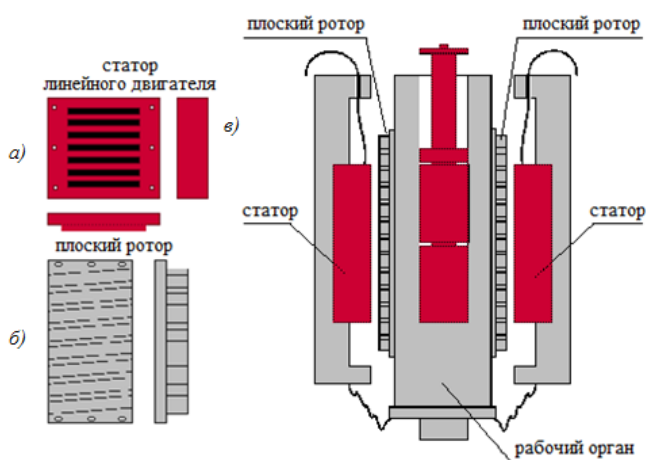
Конструкция статора и ротора линейного двигателя:
